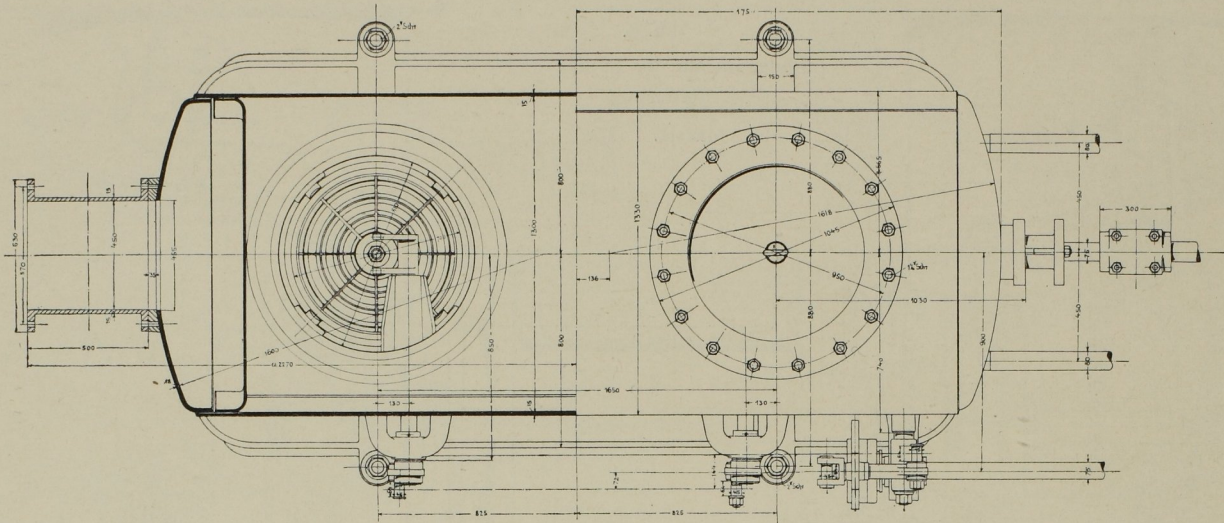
Grundriss der Pumpe. Massst. 1:30.
